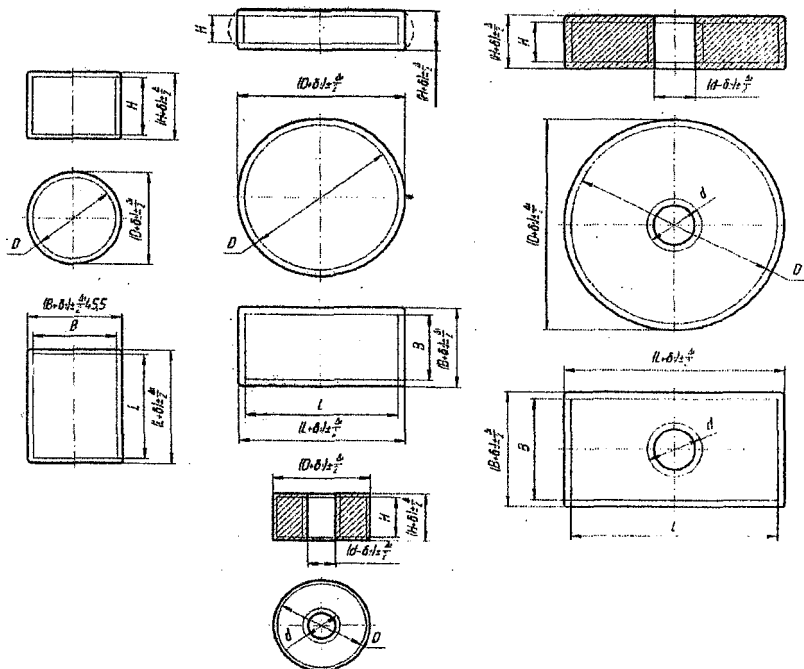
Схема назначения припусков и допусков для поковок 2-ой группы
